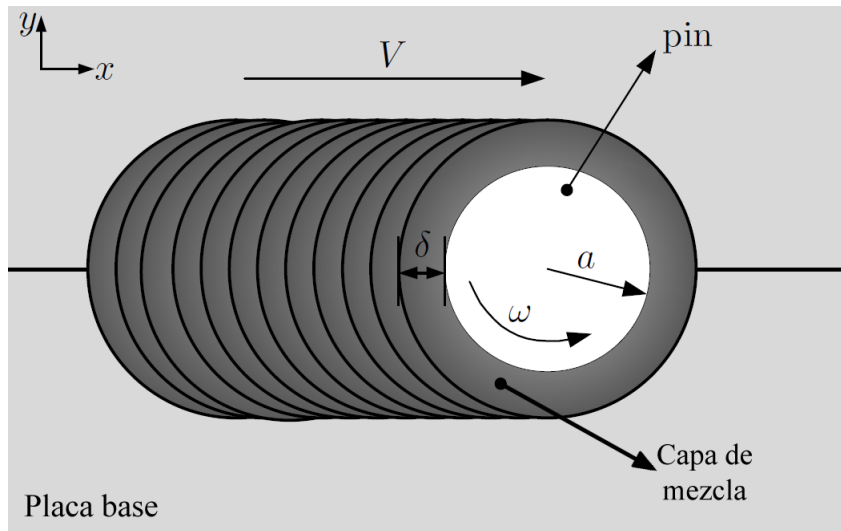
Esquema transversal del avance del pin en la soldadura incluyendo la capa de mezcla.
